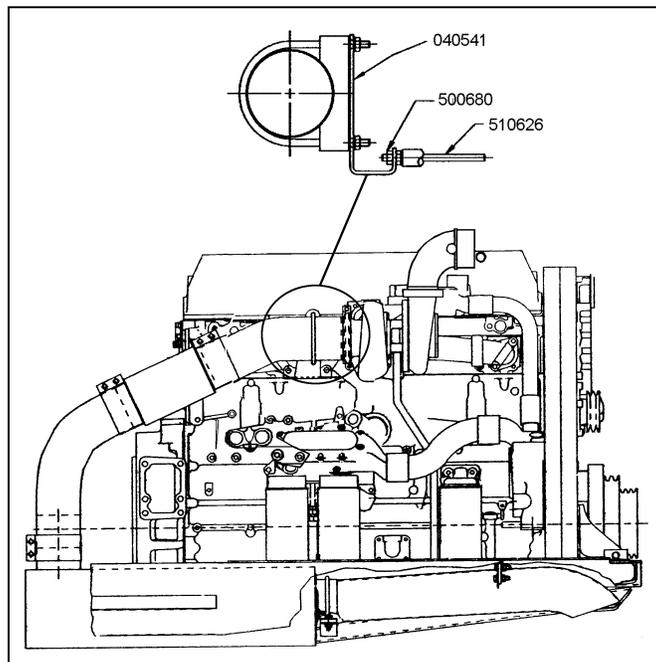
VUE DU MOTEUR - CÔTÉ TURBOCOMPRESSEUR
